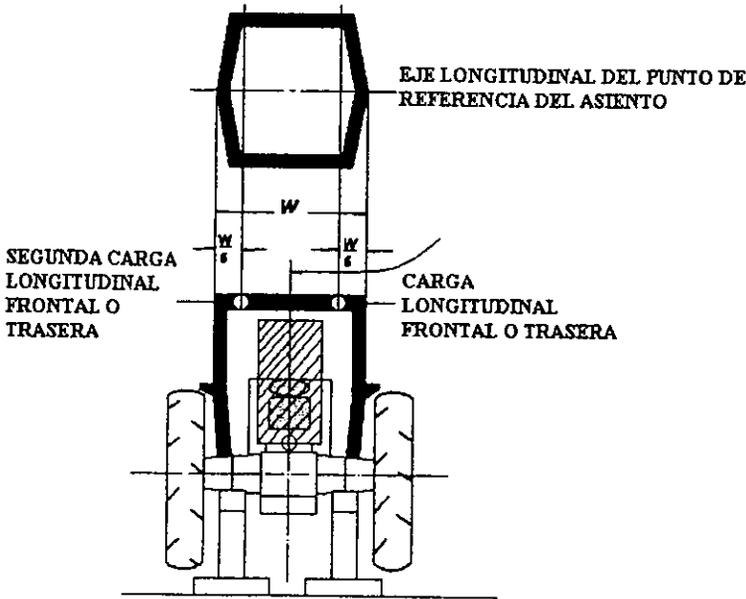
Aplicación de cargas longitudinales, vista frontal y superior
